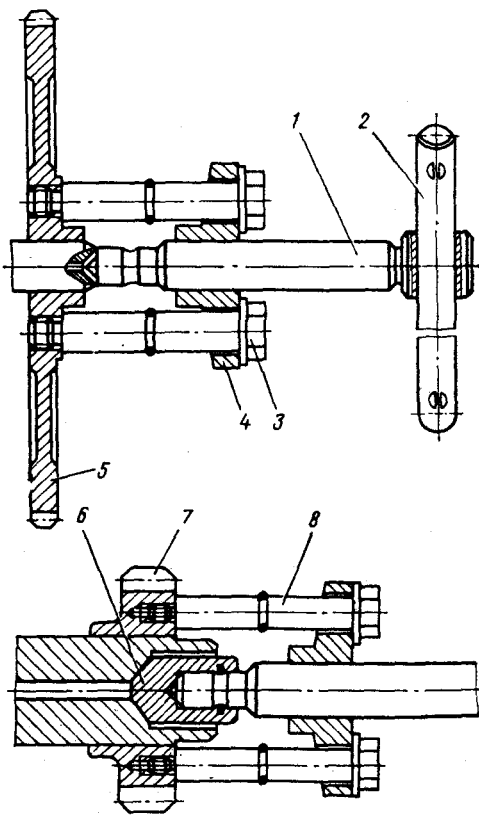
Съемник ведомой шестерни привода масляного насоса и шестерни привода компрессора И-801.02.00:
